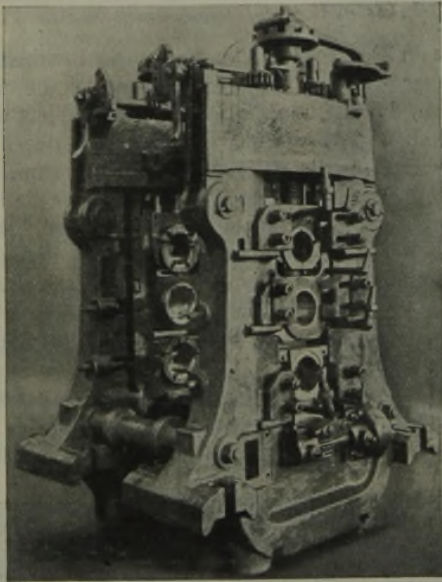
Triowalzgerüst, Mittelwalze mit Lagerbüchse.
